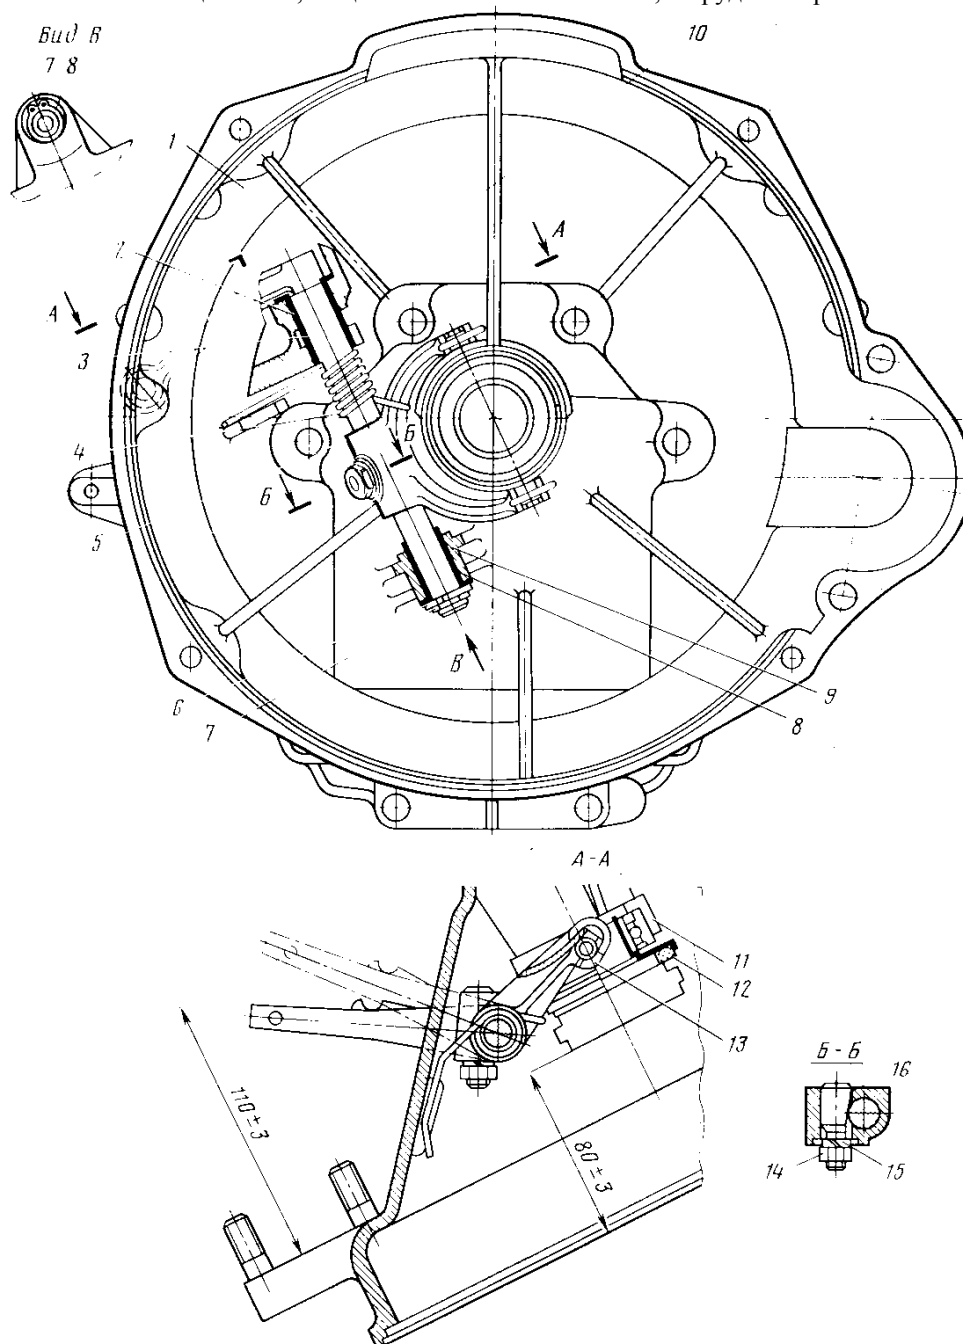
Механизм выключения сцепления: 1 — картер сцепления; 2, 8 — нижняя и верхняя втулки оси; 3 — ось вилки с рычагом в сборе; 4 — пружина; 5 — вилка выключения сцепления; 6 — регулировочная шайба; 7 — пружинное кольцо; 9, 10 — нижний и верхний приливы; 11 — обойма подпятника; 12 — подпятник; 13 — соединительное звено; 14 — гайка; 15 — шайба; 16 — клин крепления вилки.
